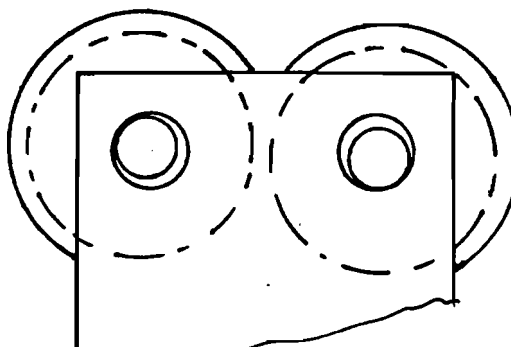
Voorbeeld van speling veroorzaakt door asafstand-afwijkingen door secundaire oorzaken.
